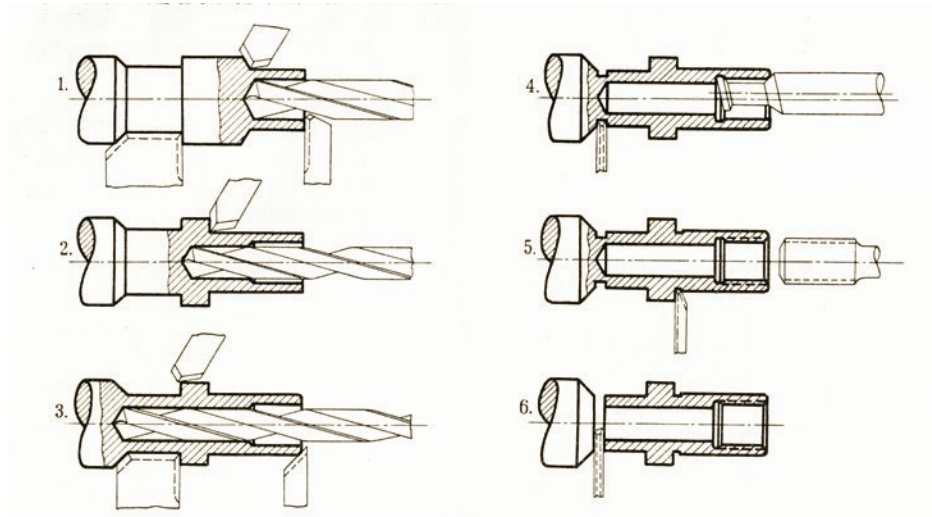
Bearbeitungsplan für die Herstellung eines Gewindestücks auf einem mechanisch gesteuerten Sechsspindler aus den 1930er Jahren [FIN38]
